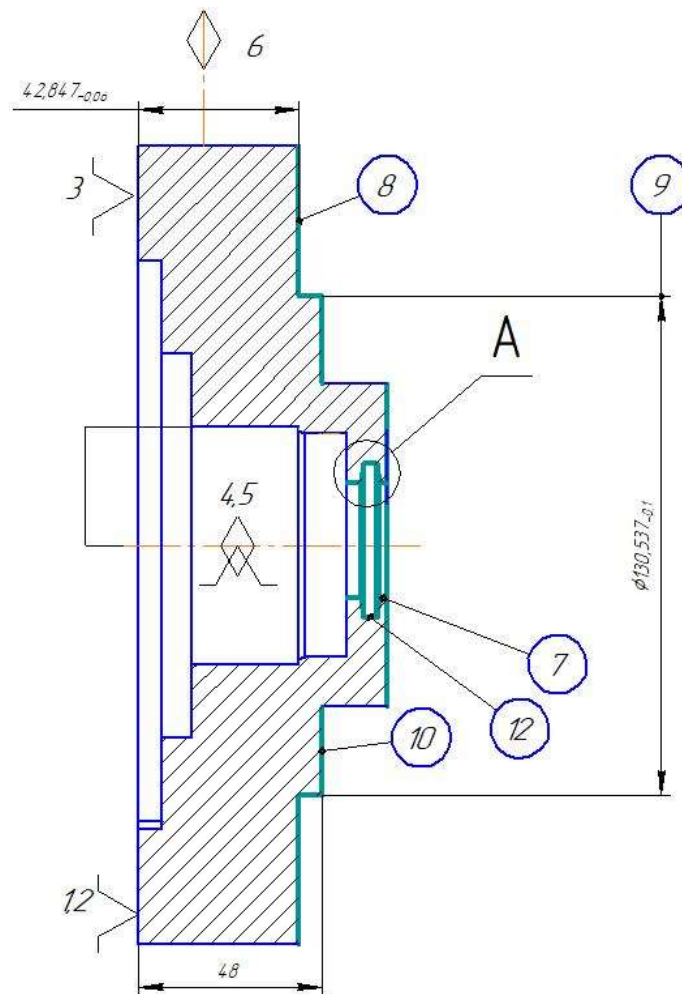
Ескіз механічної обробки із схемою базування (операція 010)
